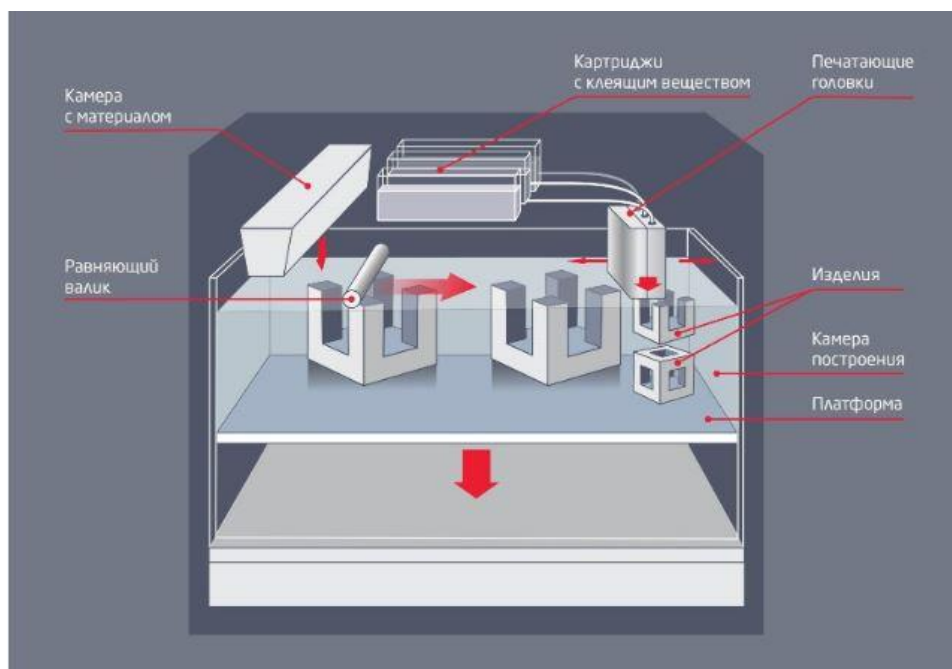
ColorJet Printing: конструкция 3D-принтера
